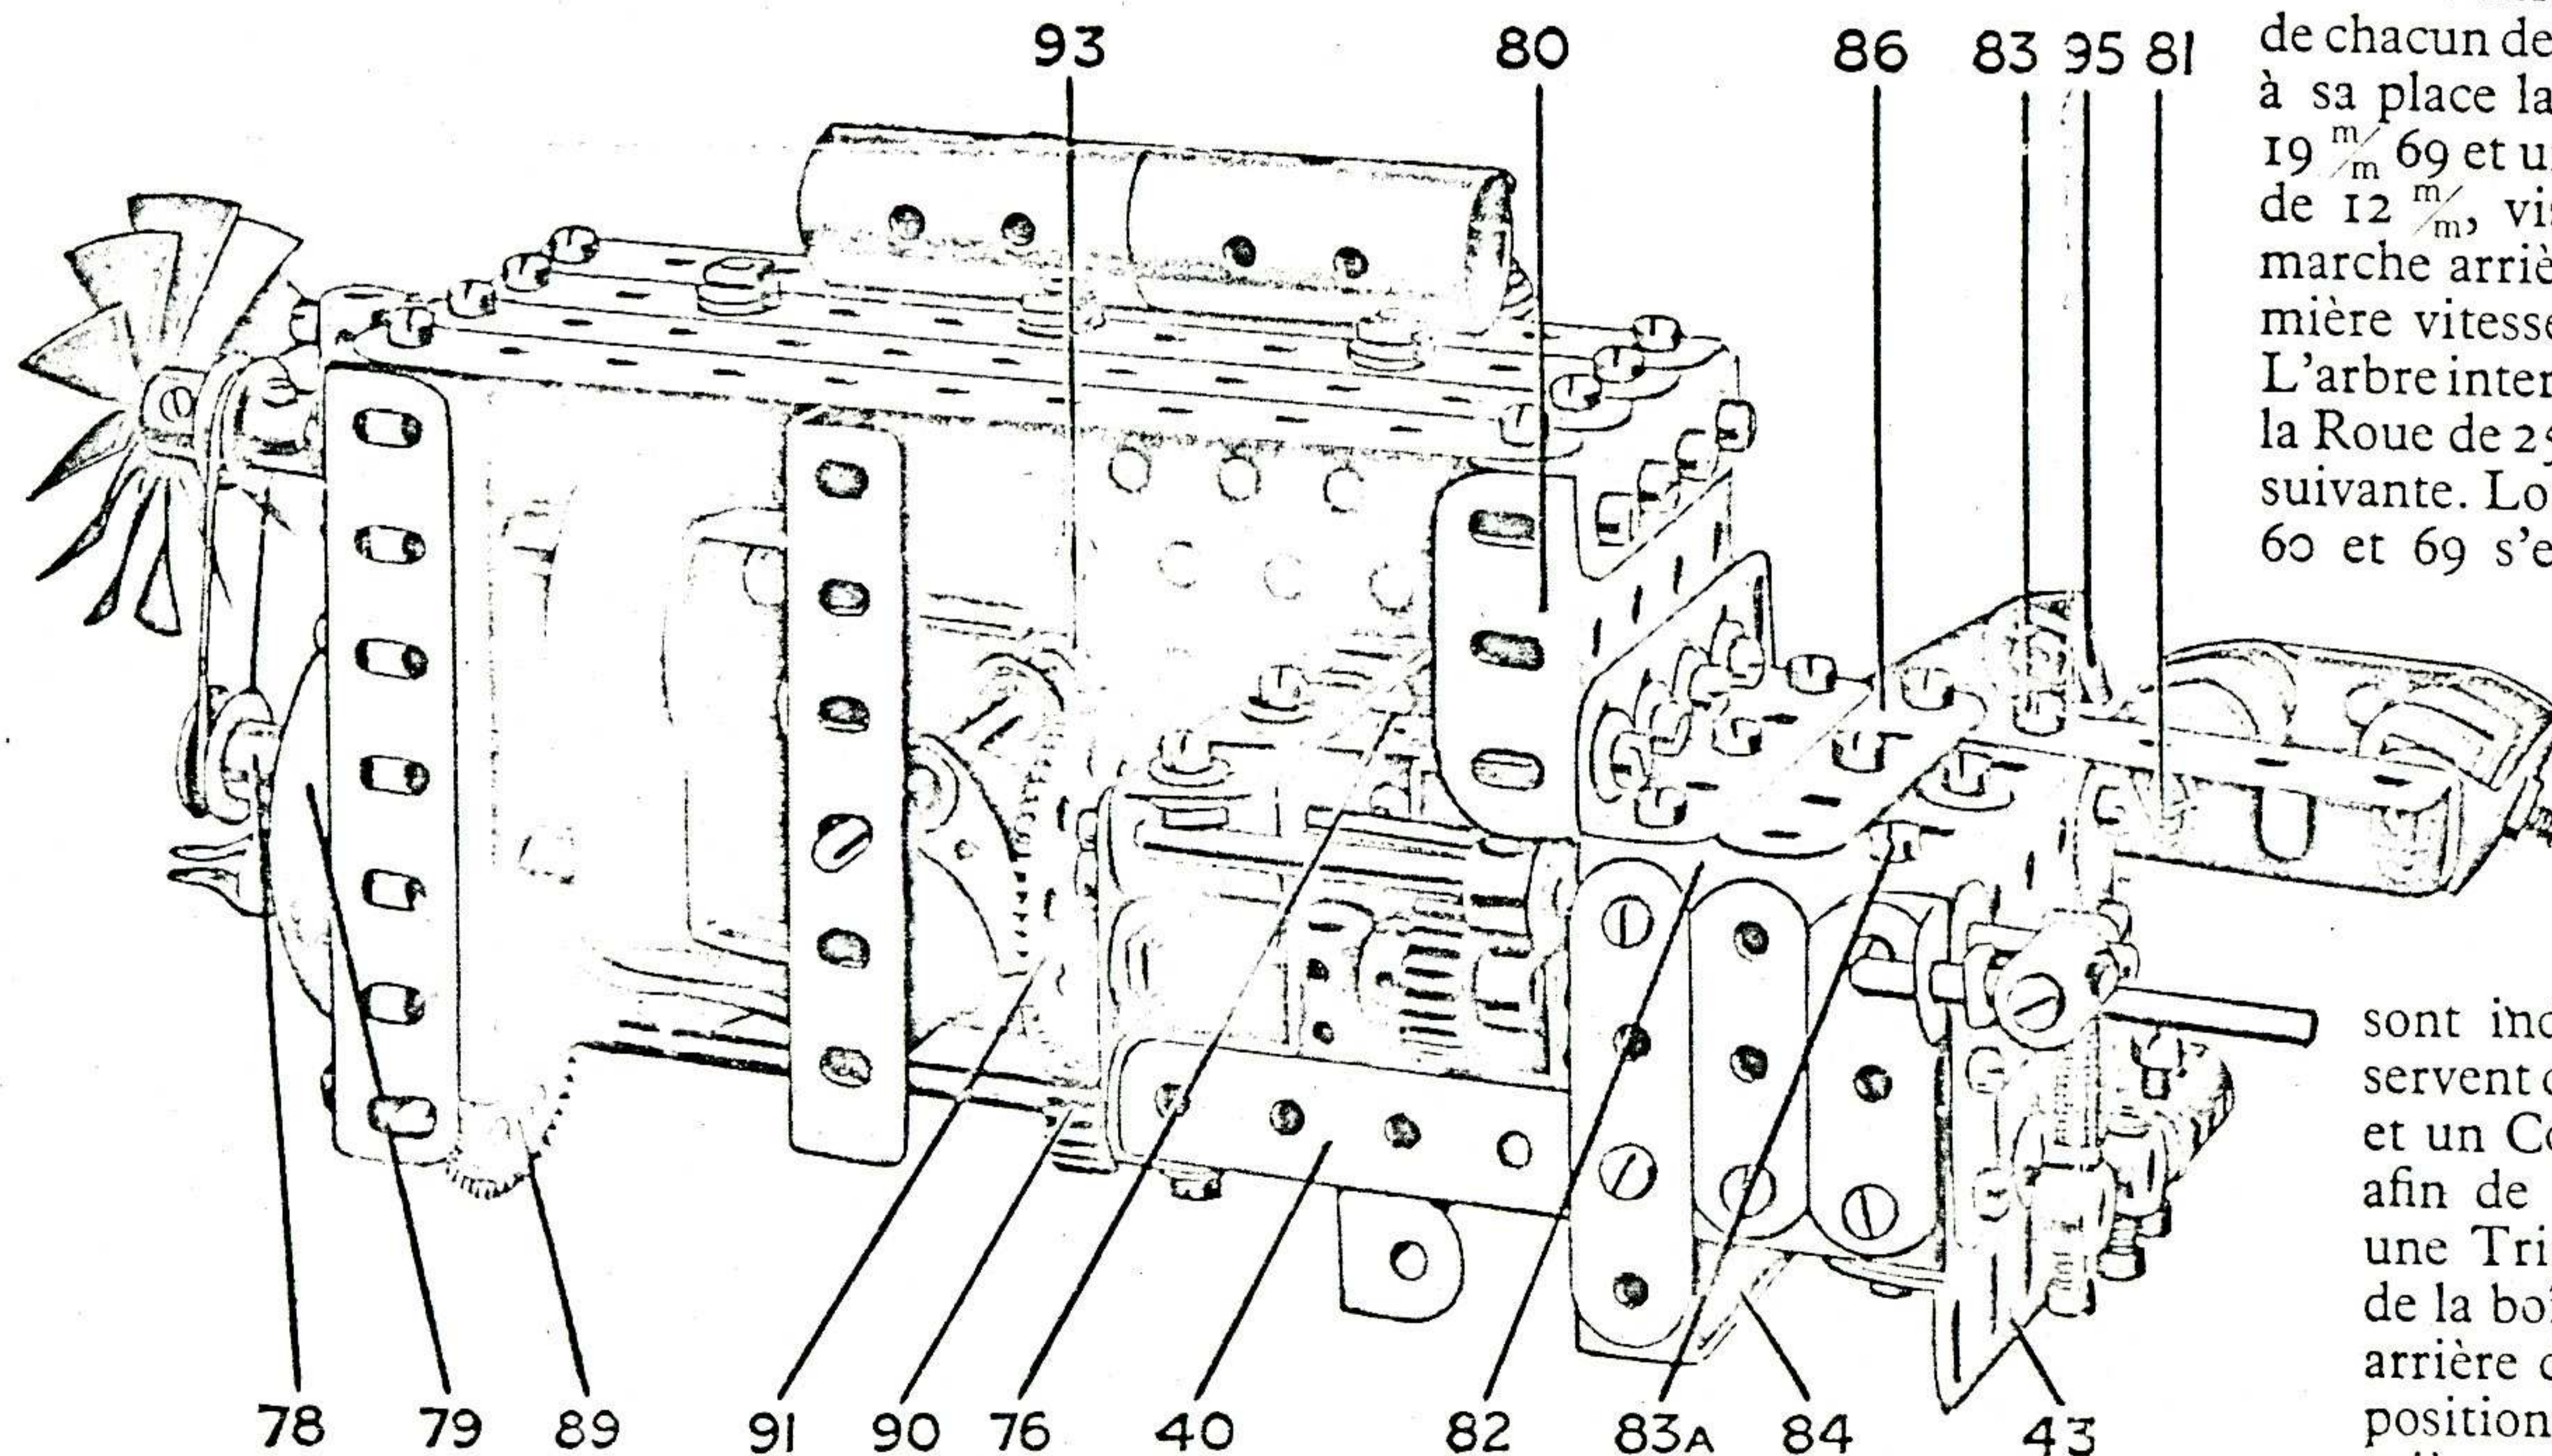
Le bloc moteur. Une des parois est enlevée pour mettre à découvert le mécanisme
